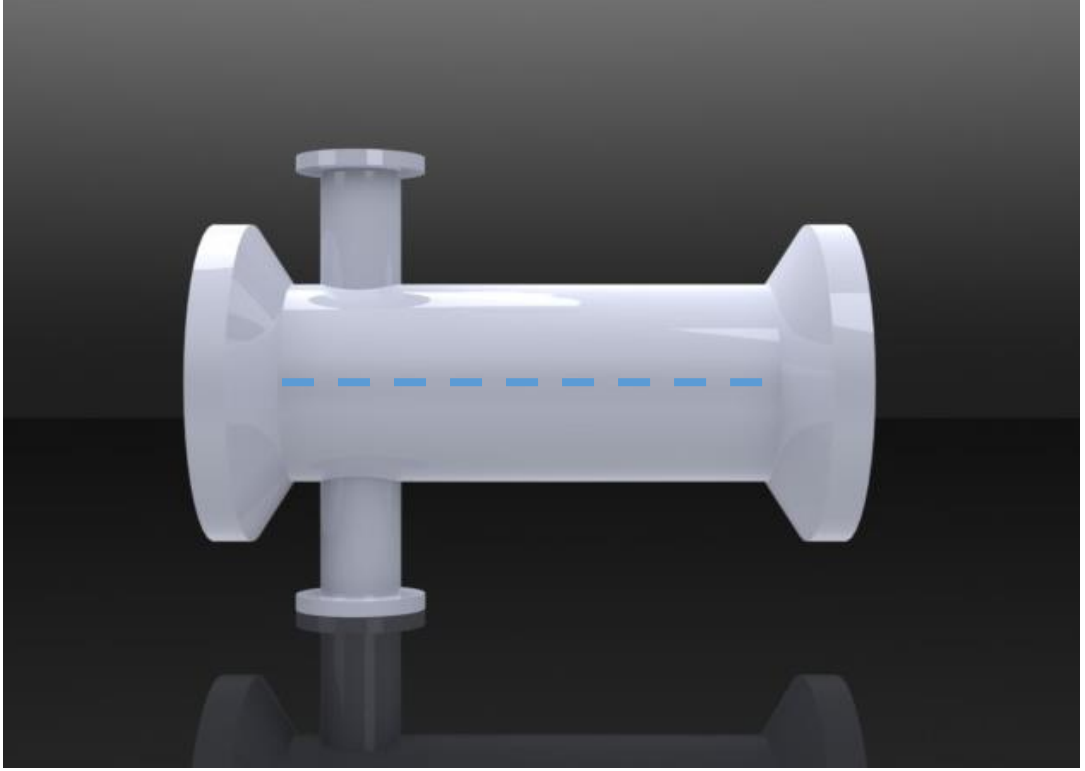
Ön kafa flanşı kaynaklı ve kapağı cıvatalı
